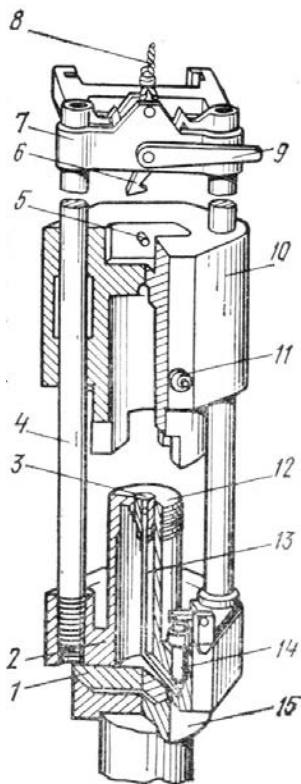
Штанговый дизель-молот: 1 – сферическая пята; 2 – основание; 3 – форсунка распылительная; 4 – штанга направляющая; 5 – палец; 6 – крюк; 7 – траверса захвата (кошки); 8 – канат лебедки копра; 9 – рычаг сброса; 10 – цилиндр; 11 – стержень; 12 – поршень; 13 – топливопровод; 14 – приводной рычаг топливного насоса; 15 – наголовник
